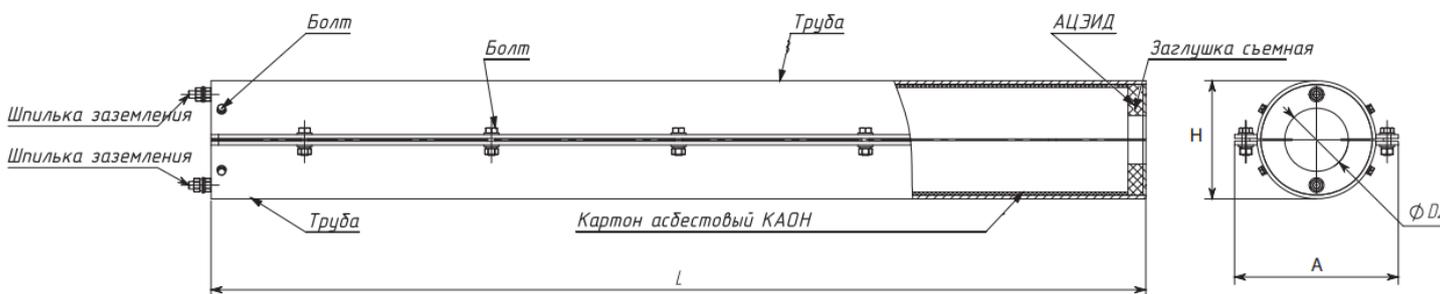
Кожух защитный разъемный типа КСР-2М
